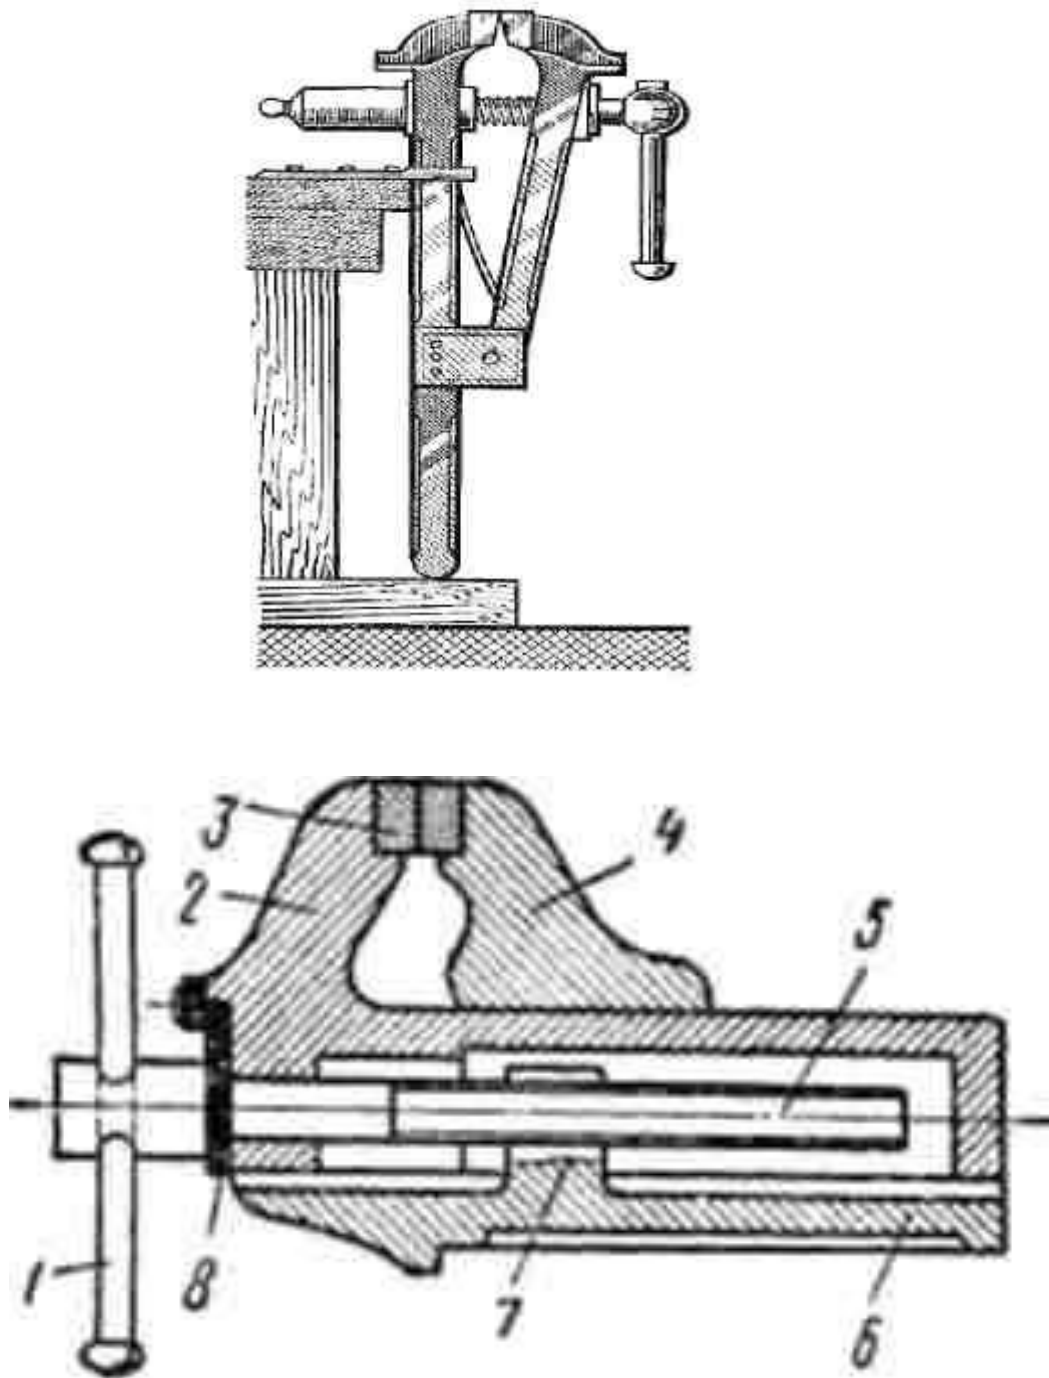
Стільцеві та неповоротні паралельні лещата: 1 – важіль; 2 – рухома губка; 3 – пластини; 4 – нерухома губка; 5 – гвинт; 6 – основа; 7 – гайка; 8 – корпус рухоми губки
